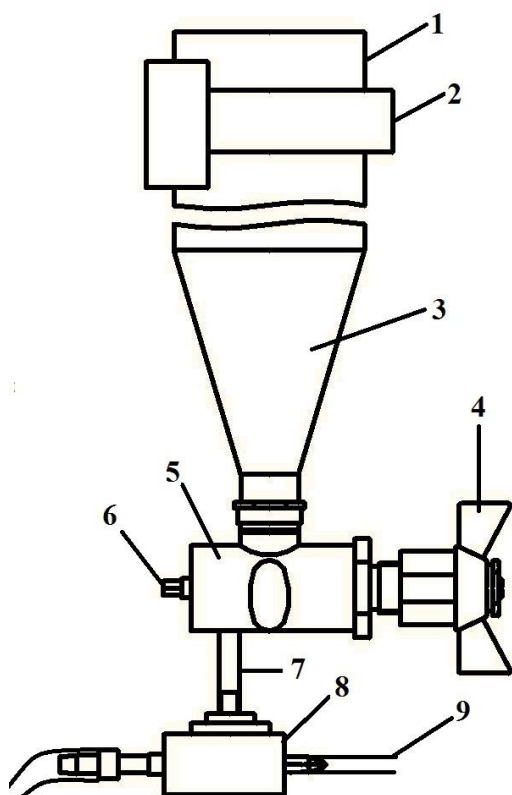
Схема порошкового питателя установки для СГП-наплавки
